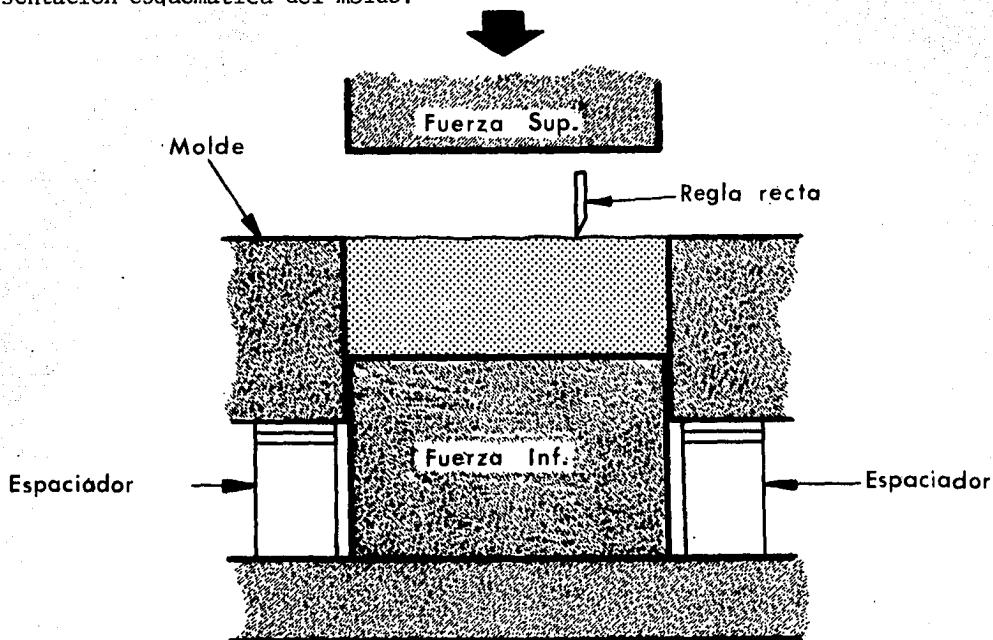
MOLDEO DE PLACA T.F.E.
